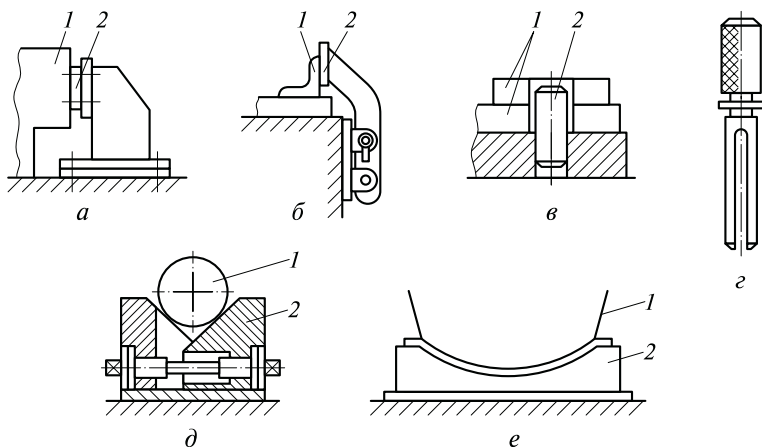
Установочные элементы в сборочных приспособлениях:
